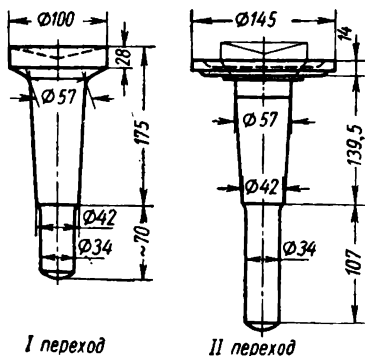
Двухпереходная штамповка поковки ведомого вала
